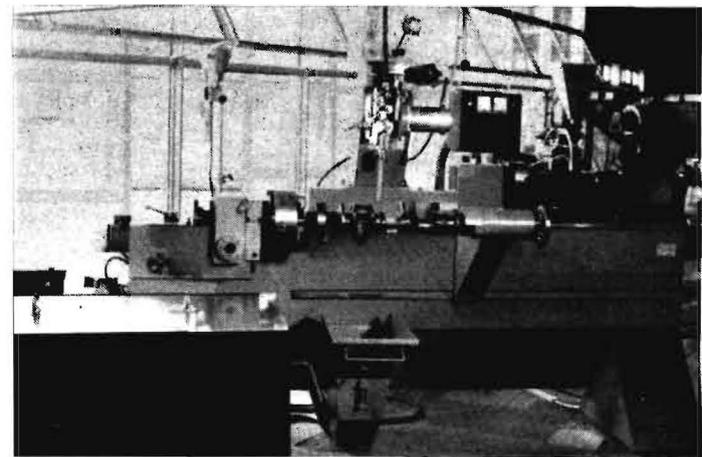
Anlage 011-1-00 Remdeta zum UP-Auftragschweißen von Kurbelwellen
